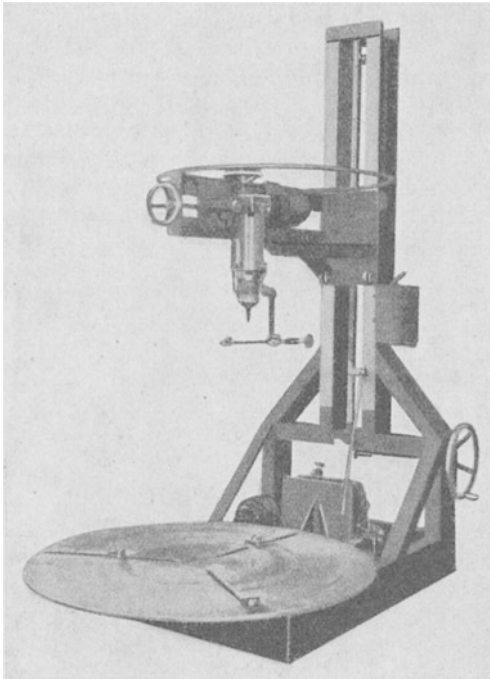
Selbsttätige Schweißmaschine für Faßschweißung.
